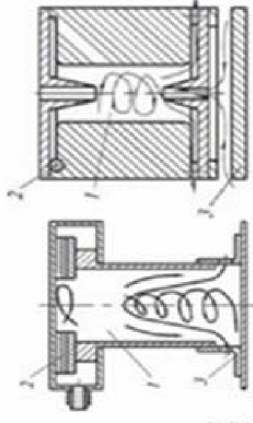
Вихрові захватні пристрої з пневматичним вихортуванням
